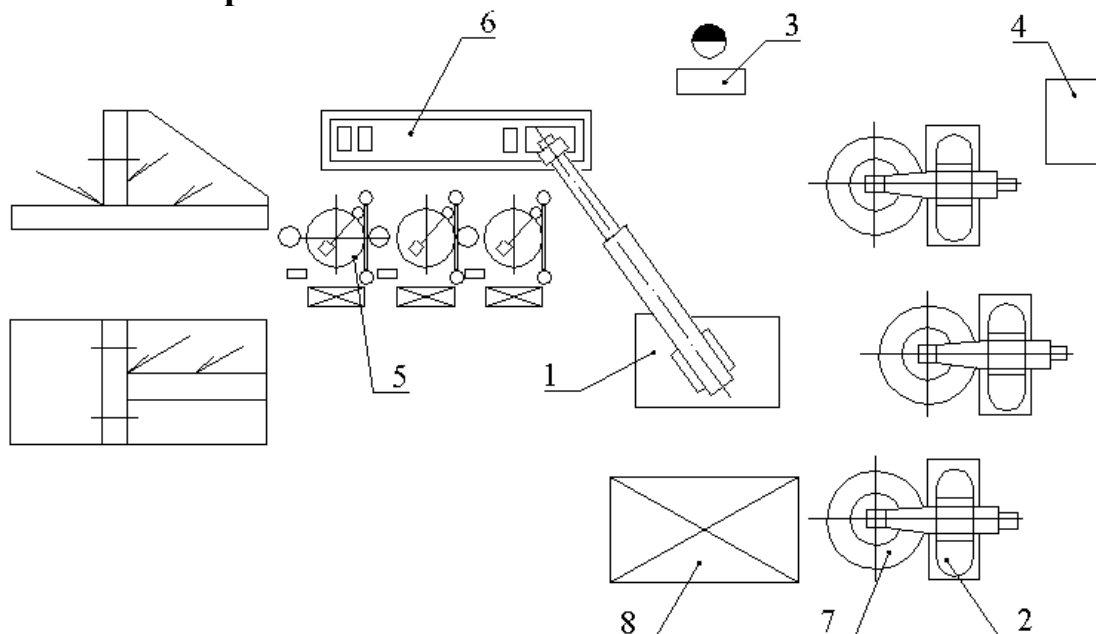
ПР мод. "Универсал 15М"; 2 - сварочный ПР мод. 109А (3 шт.); № - пульт управления; 4 - устройство управления; 5 - позиция предварительной сборки (3 шт.); 6 - конвейер (6 шт.); 7 - стол - кантователь (3 шт.); 8 - склад - стеллаж изделий.
